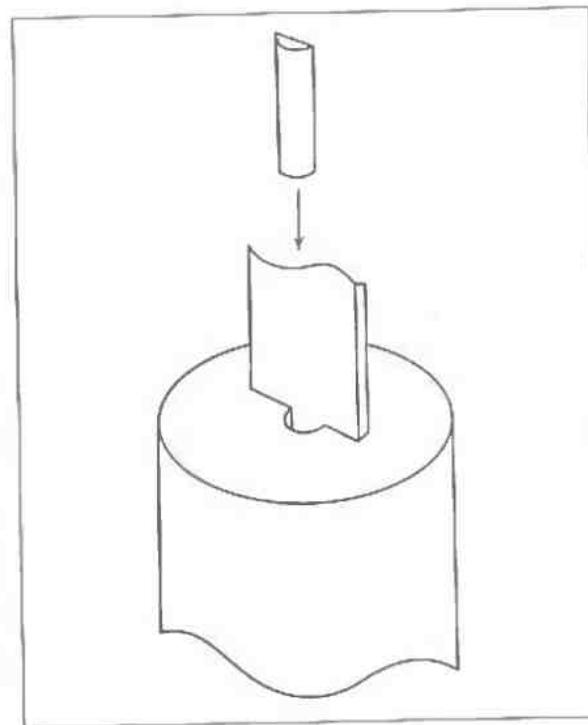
Заделка отверстий в заготовке рукояти фасонными вставками
